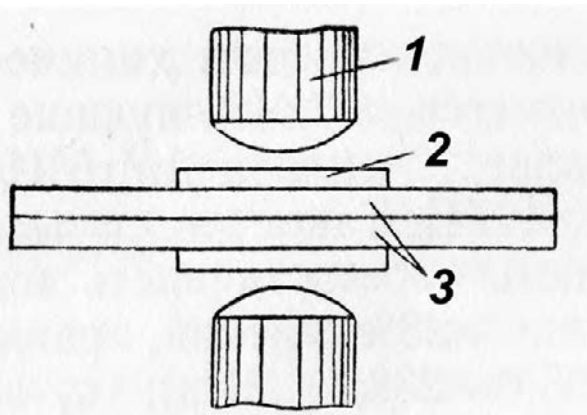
Схема точечной сварки алюминия с использованием прокладок из нержавеющей стали 12Х18Н9: 1 — электрод; 2 — прокладка; 3 — свариваемые детали
